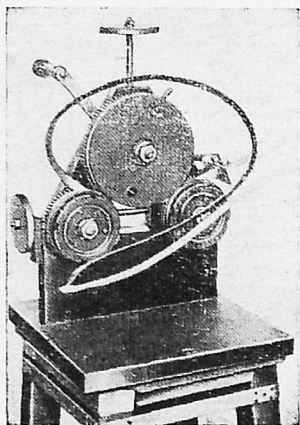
Приспособление для вальцовки на ребро медной ленточки.
